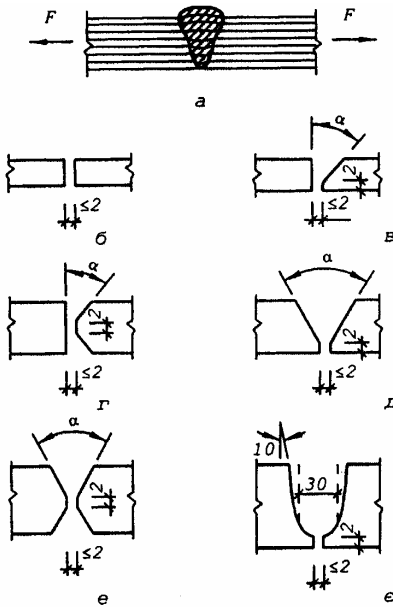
Стовкові шви і обробка граней перед зварюванням:
